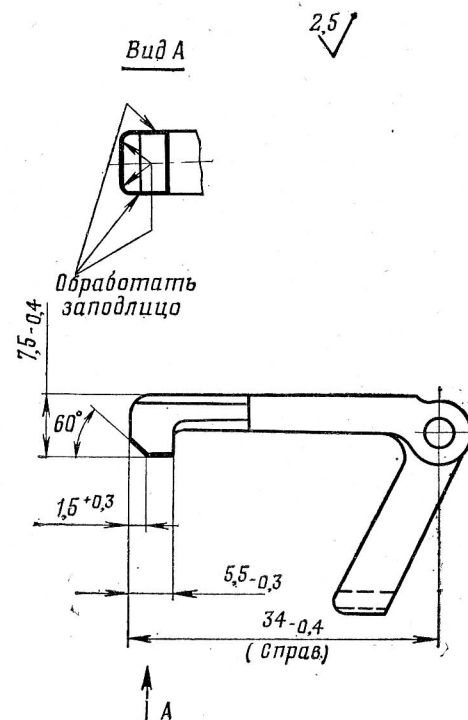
Обработка зуба зацепа пулемета РПКС74 с ночным прицелом после наплавки
